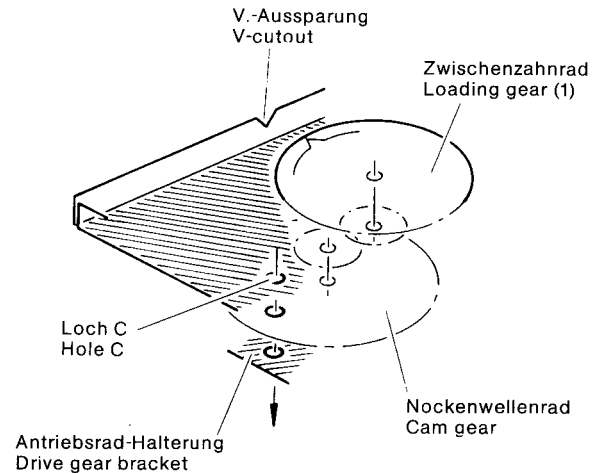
Nockenwellenrad/Zwischenzahnrad / Cam gear/loading gear (1)
